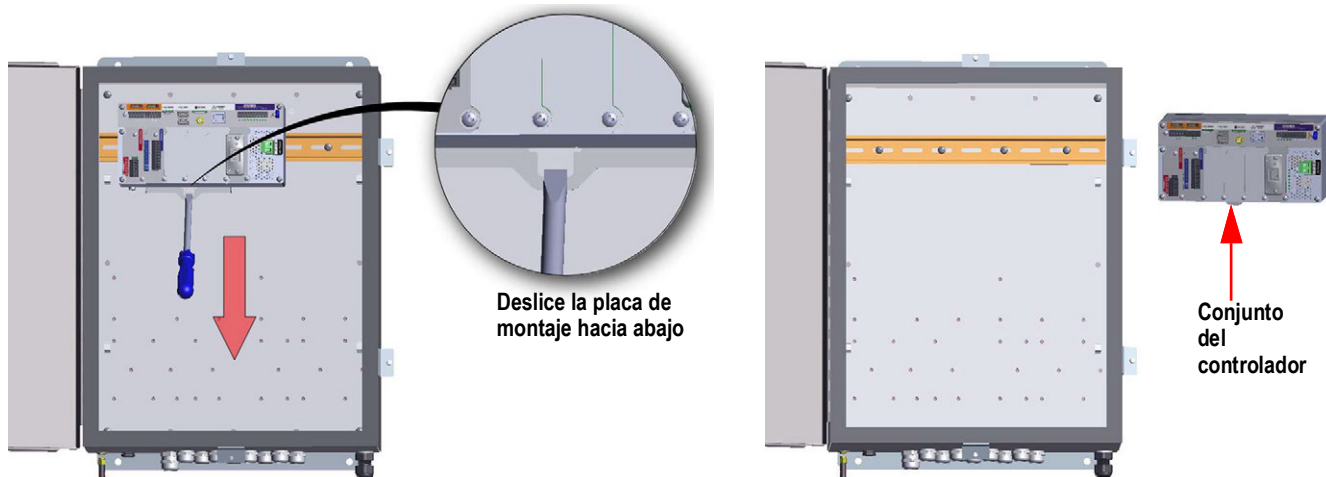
Desmontaje del conjunto del controlador - Alojamiento para pared
